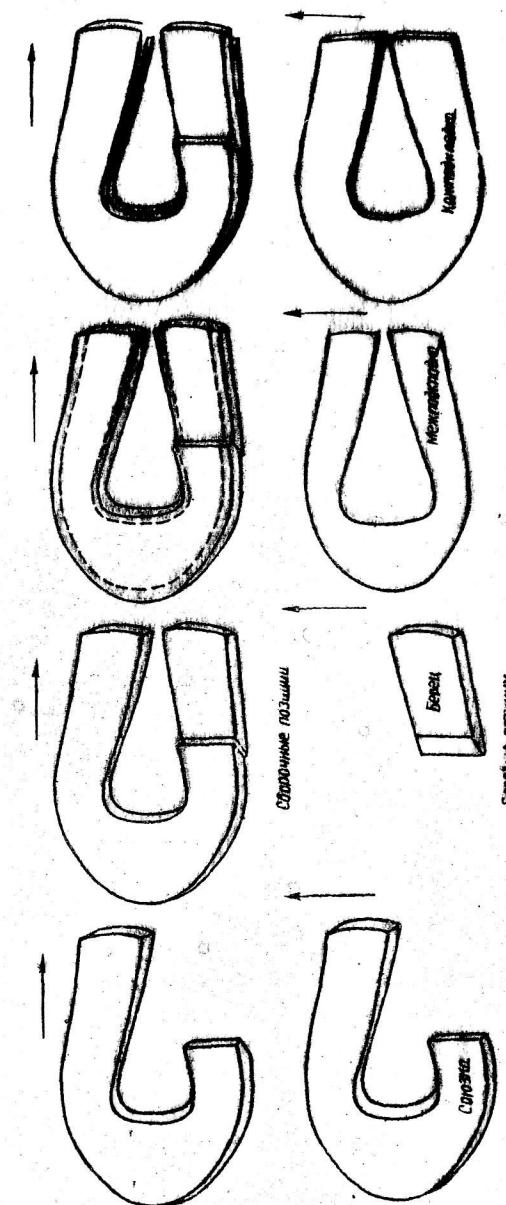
Технологическая карта сборки заготовки типа "лодочка".
